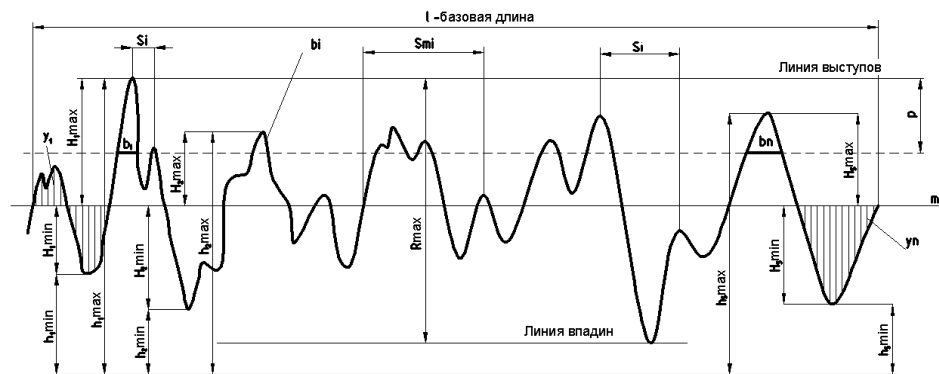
Схема шероховатости поверхности и ее элементы [29]
